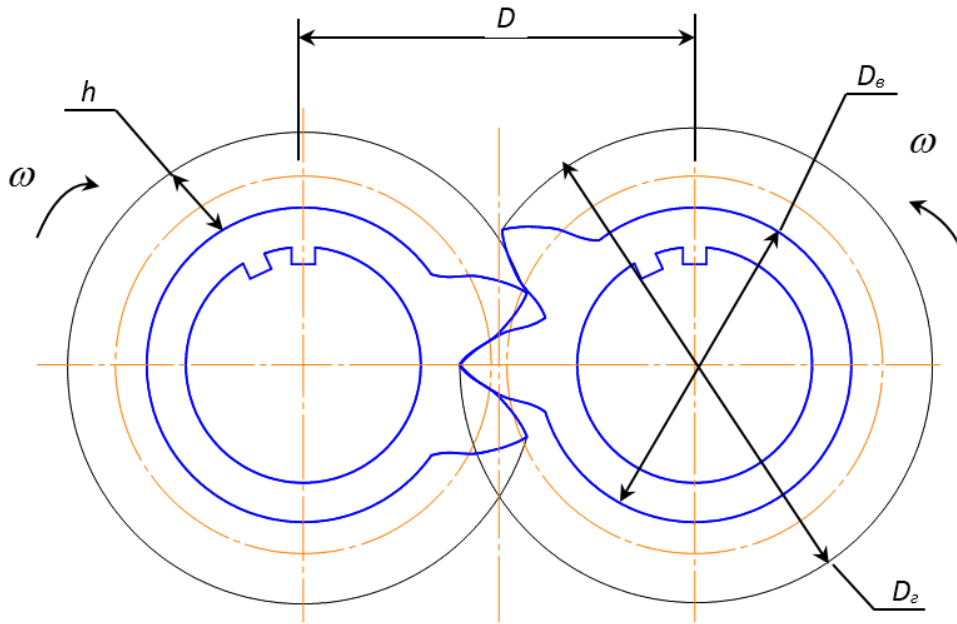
Розрахункова схема шестеренчастої дробарки
